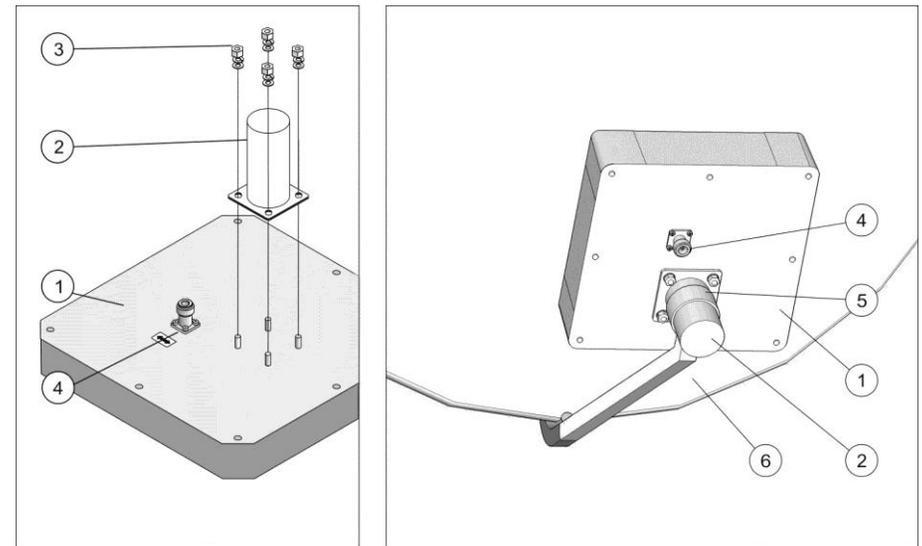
Сборка облучателя (слева) и установка в рефлектор (справа)
